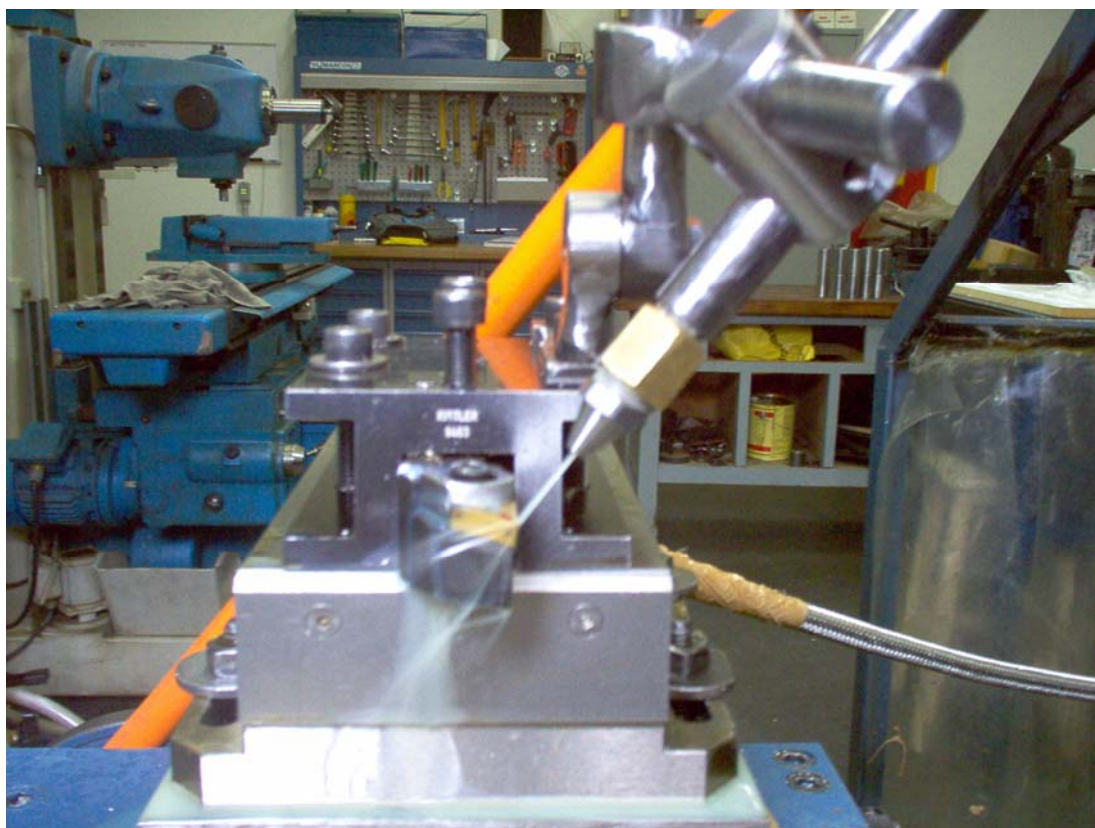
Posição 3, jato aplicado entre a peça e o cavaco.
